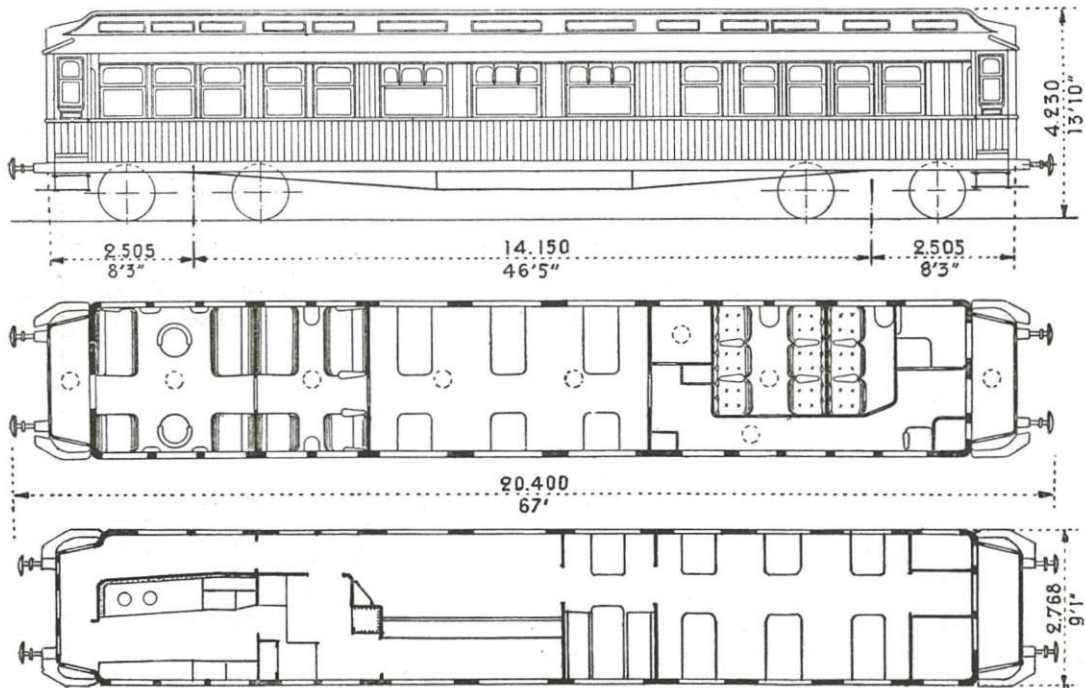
a) Elévation et plan des voitures-salon de la Compagnie des Wagons-Lits; b) Plan des voitures-bar.
